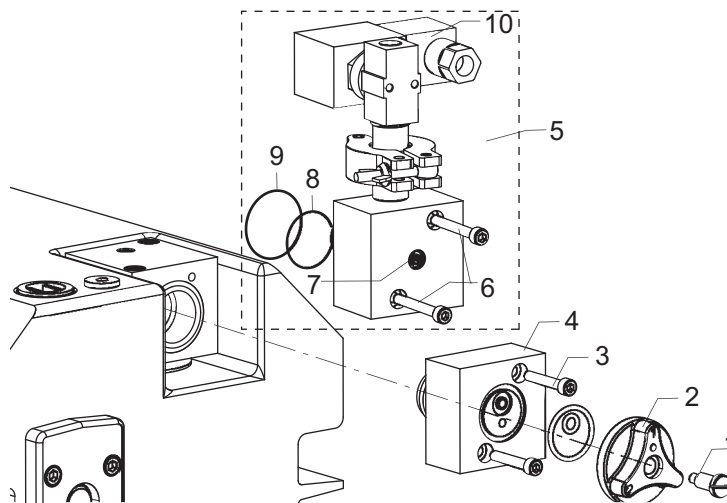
Anschluss des Magnetventils für das Gasballastventil
